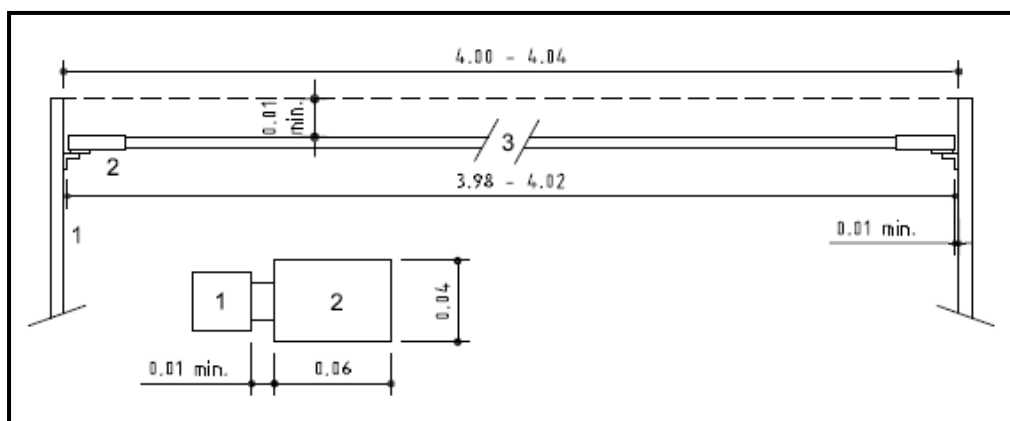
Support de barre transversale pour le saut en hauteur
